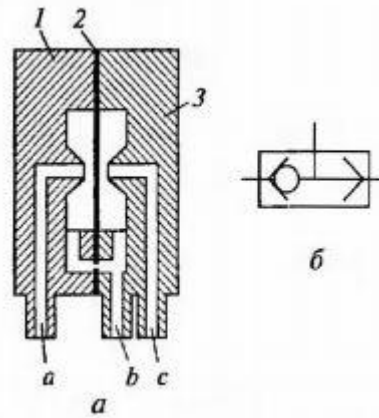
Пневмоклапан «ИЛИ» (а) и его условное обозначение (б): 1 - корпус; 2 - мембрана; 3 – крышка.
